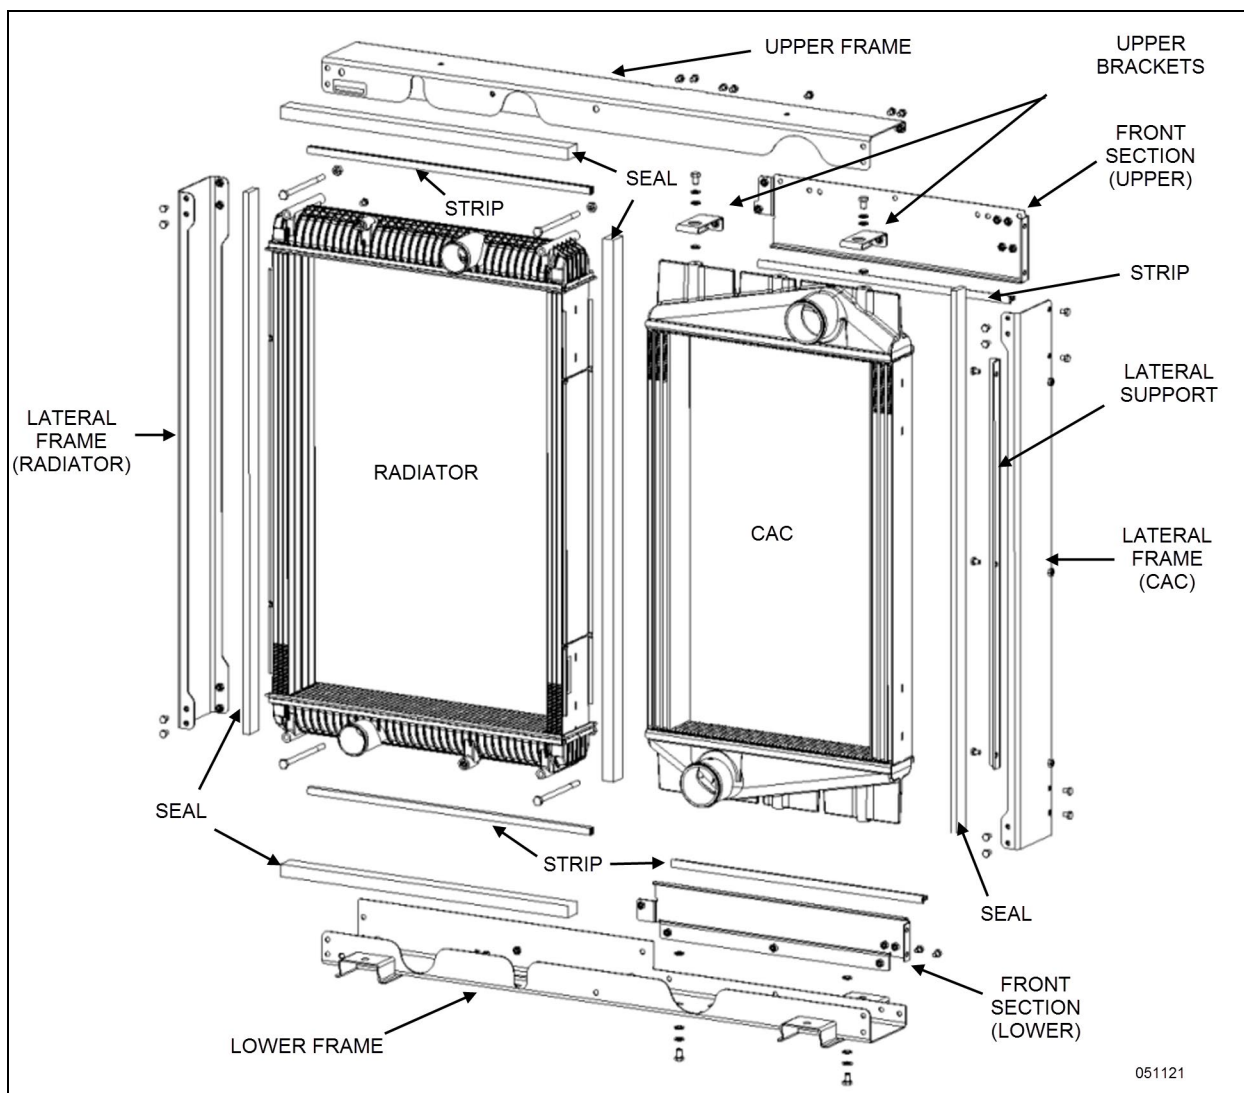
VISTA EXPLOSIONADA DEL PAQUETE DE ENFRIAMIENTO
